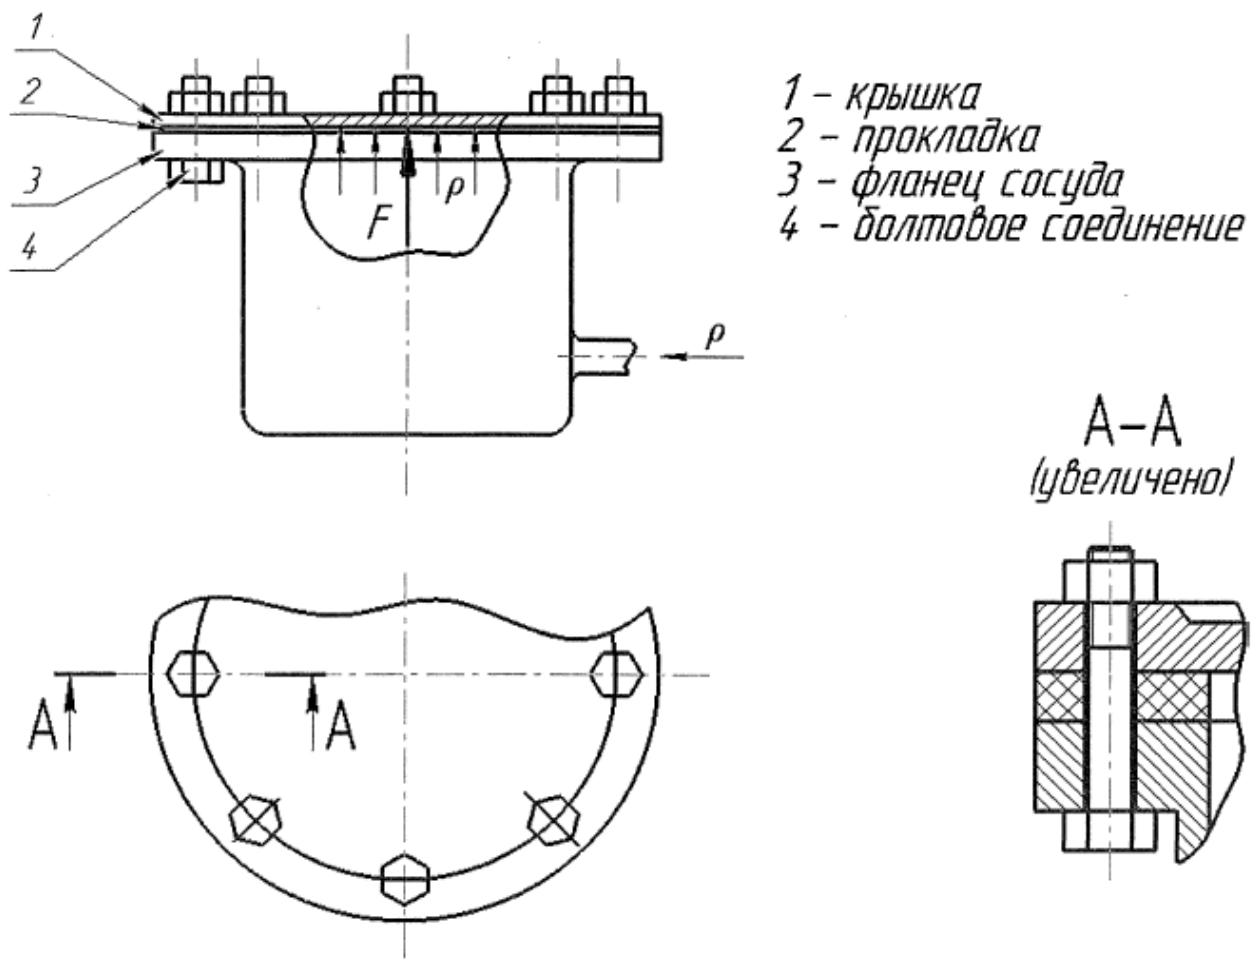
Цилиндрический сосуд с крышкой
